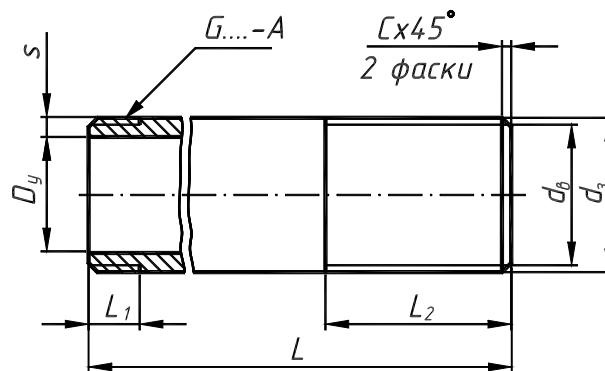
Конструктивные размеры патрубка под сгон
